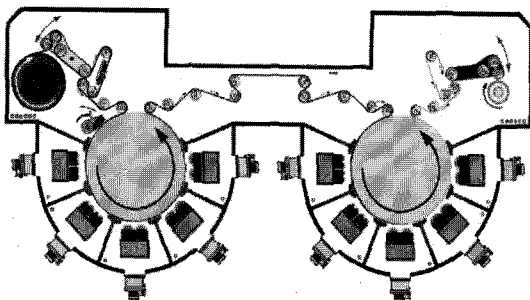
Applied Film社의 Roll-to-Roll Vacuum Deposition System.
